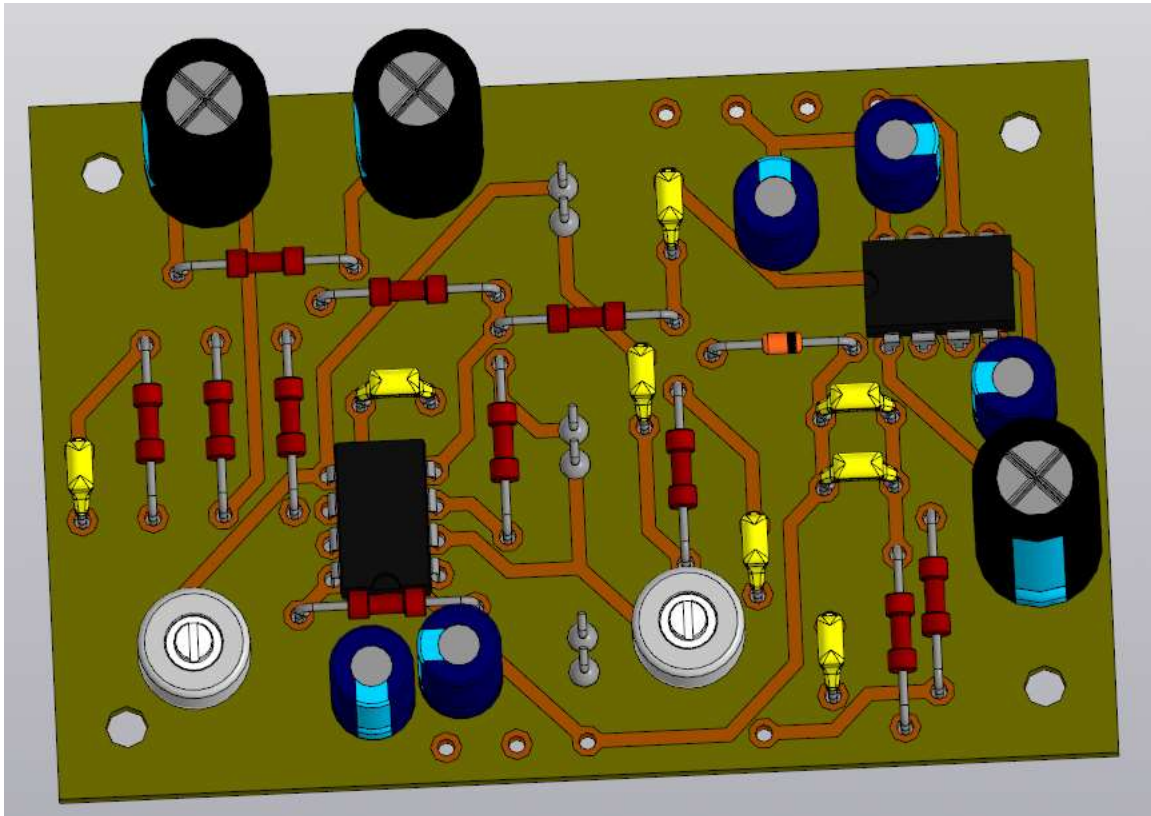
3D модель пристрою, вузол друкований
